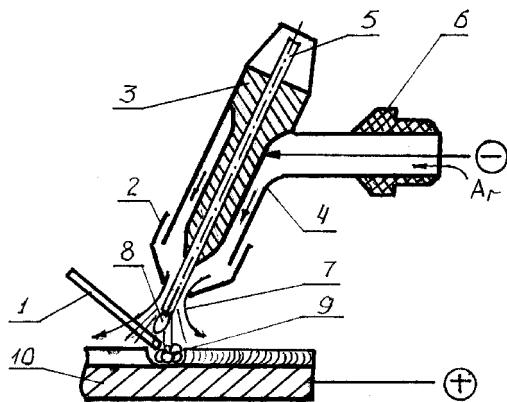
Схема электродержателя для аргоно-дуговой сварки: 1 - присадочный пруток; 2 - сопло; 3 - токоведущий мундштук; 4 - корпус; 5 - электрод; 6 - рукоятка; 7 - атмосфера защитного газа, 8 - сварочная дуга, 9 - ванна расплавленного металла; 10 - деталь
